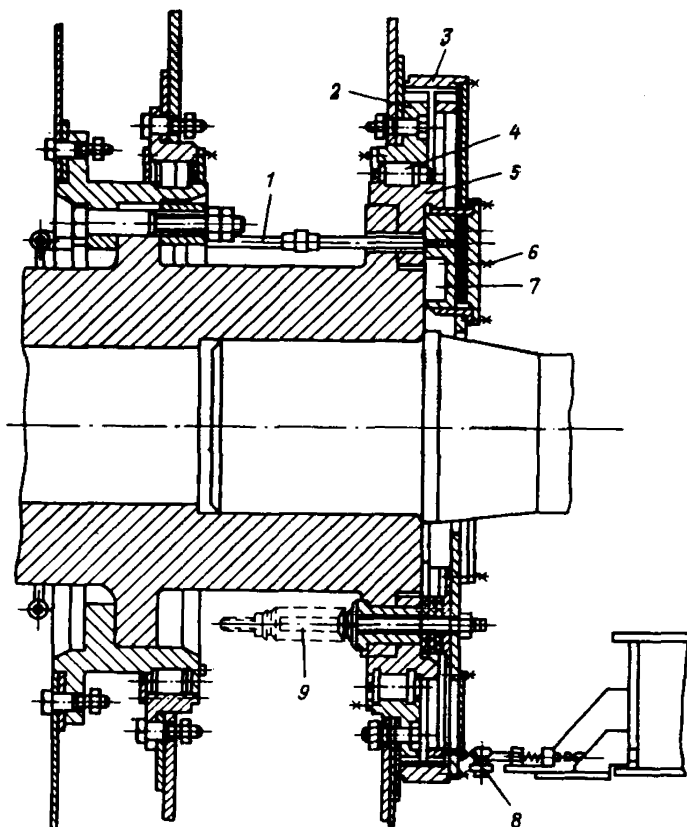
Механизм перестановки зубчатый безрычажный на роликовых опорах:
